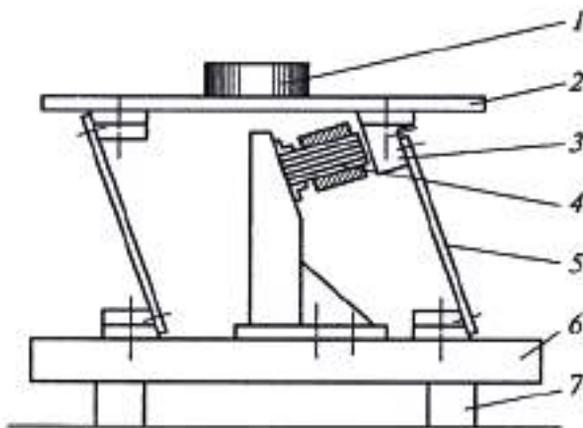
Принципиальная схема ВЗУ с прямолинейным лотком: 1 – заготовка; 2 – лоток; 3 – якорь; 4 – вибратор; 5 – подвеска; 6 – основание; 7 – амортизатор
